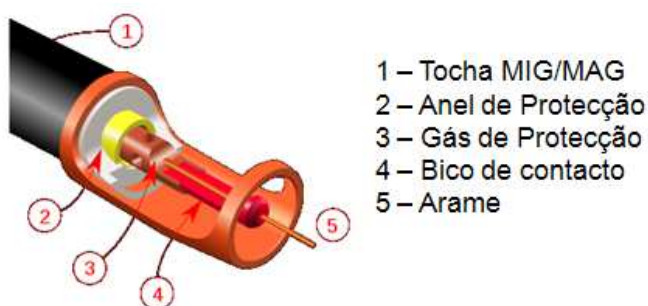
Tocha de soldadura MIG/MAG [7].
